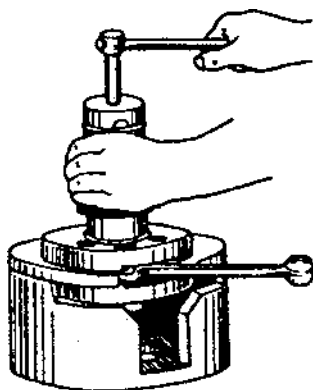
Снятие подшипника с полуоси коленчатого вала ИЖ П-5
